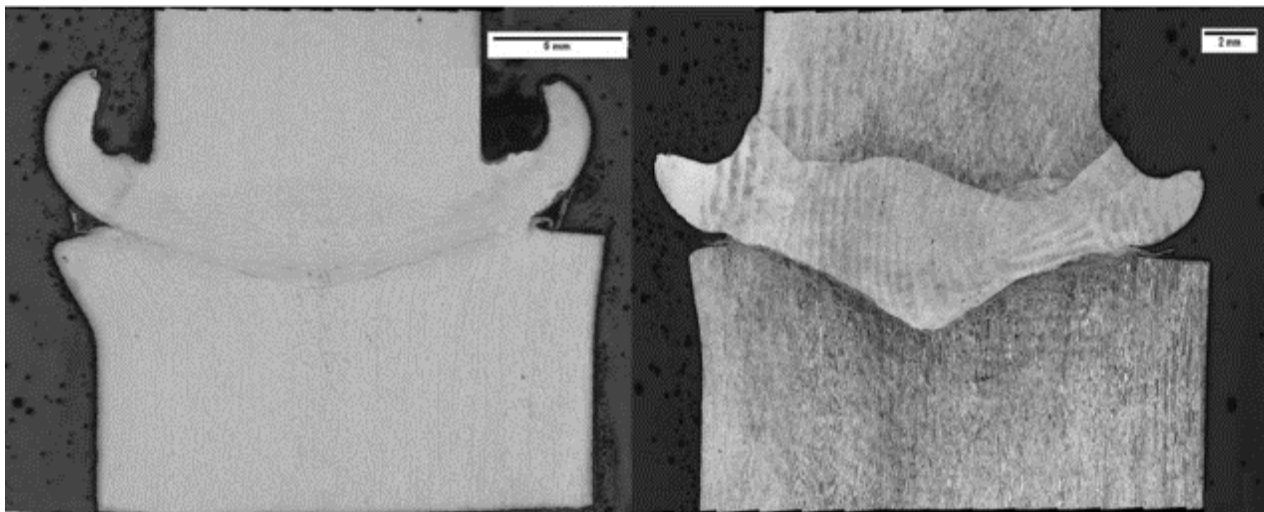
Macroestruturas das juntas soldadas. A amostra 1 (esquerda) e amostra 2 (direita) ambas apresentam uma boa união metalúrgica.
